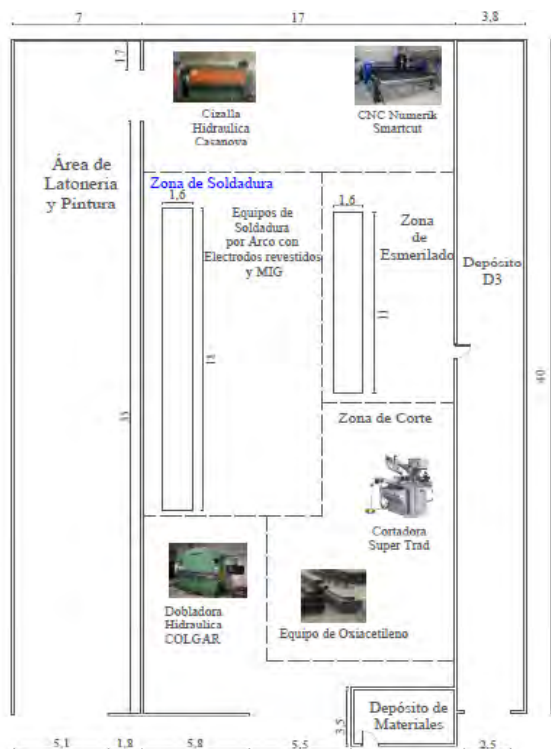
Plano de Taller Metal-Mecánico (dimensiones en m).
